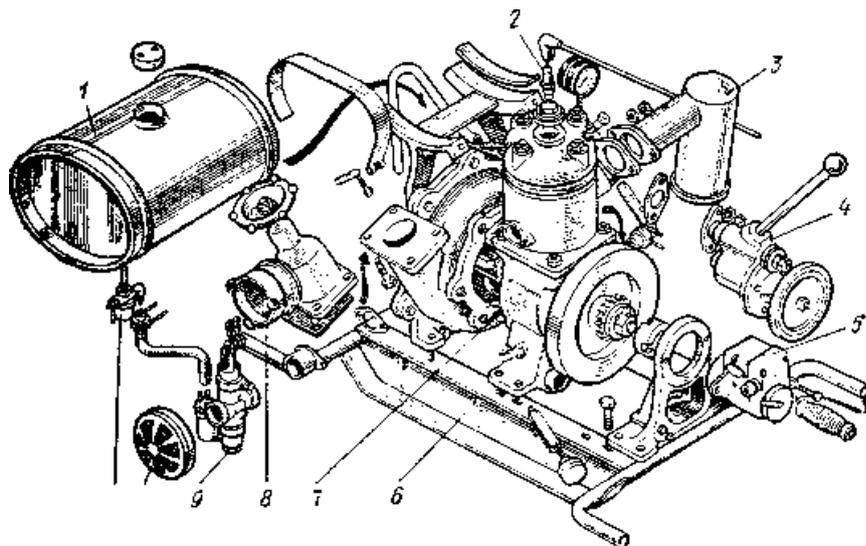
Мотопомпа МП-600А: 1 – топливный бак; 2 – отверстие для свечи; 3 – глушитель; 4 – ротационный вакуум-аппарат; 5 – магнето; 6 – основание вакуумметра; 7 – центробежный насос; 8 – напорный патрубок; 9 – карбюратор; 10 – воздухоочиститель; 11 – кран
